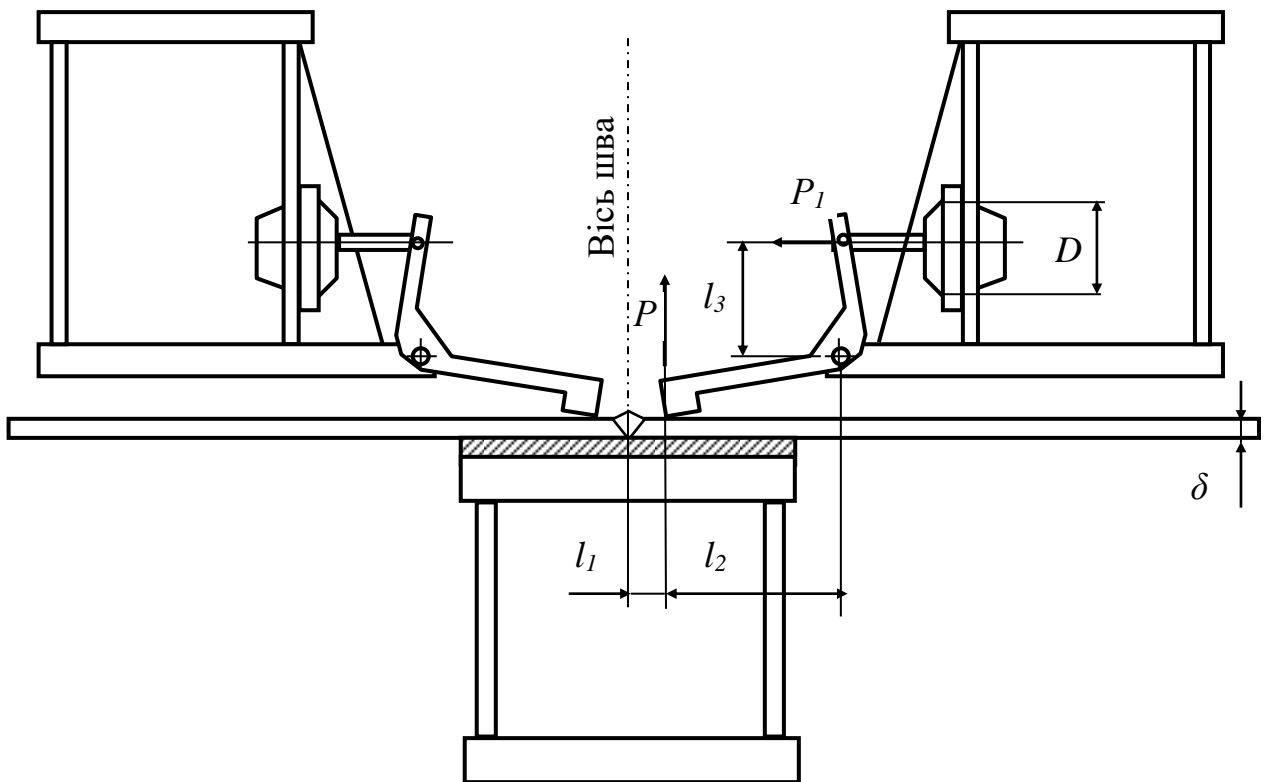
Схема для розрахунку параметрів станда для зварювання деталей автозчепи стиковим способом
